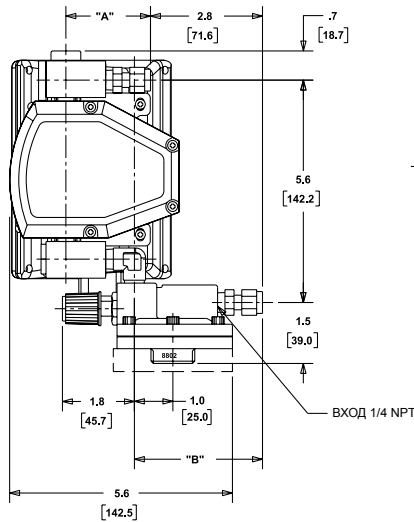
Размеры для резьбовых соединений MT3750C с передатчиком или индуктивным выключателем предельных значений
